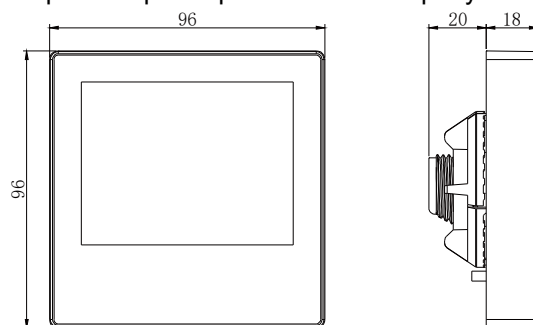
Внешний вид и габаритные размеры модуля дисплея D1
